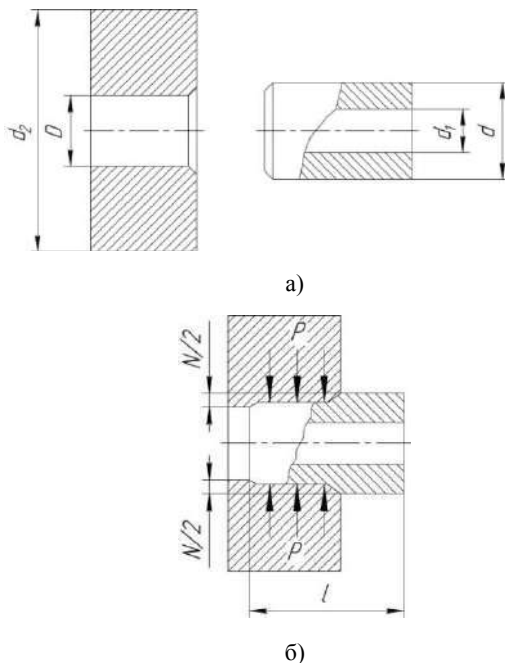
Соединение полого вала и втулки, образующих посадку с натягом: а – до сборки; б – после сборки
